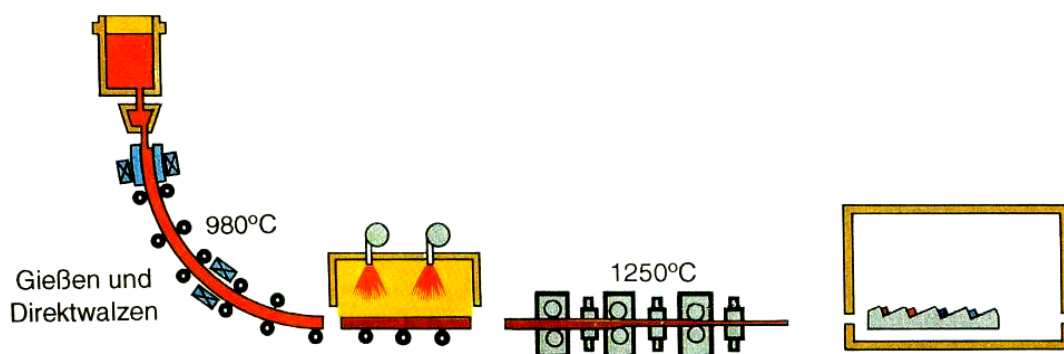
Stranggießanlage – Ausgleichsofen – Direktwalzanlage – Kühlbett [Bal93]
